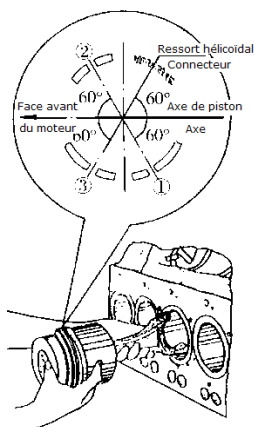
Position d'assemblage des écarterments des segments de piston
